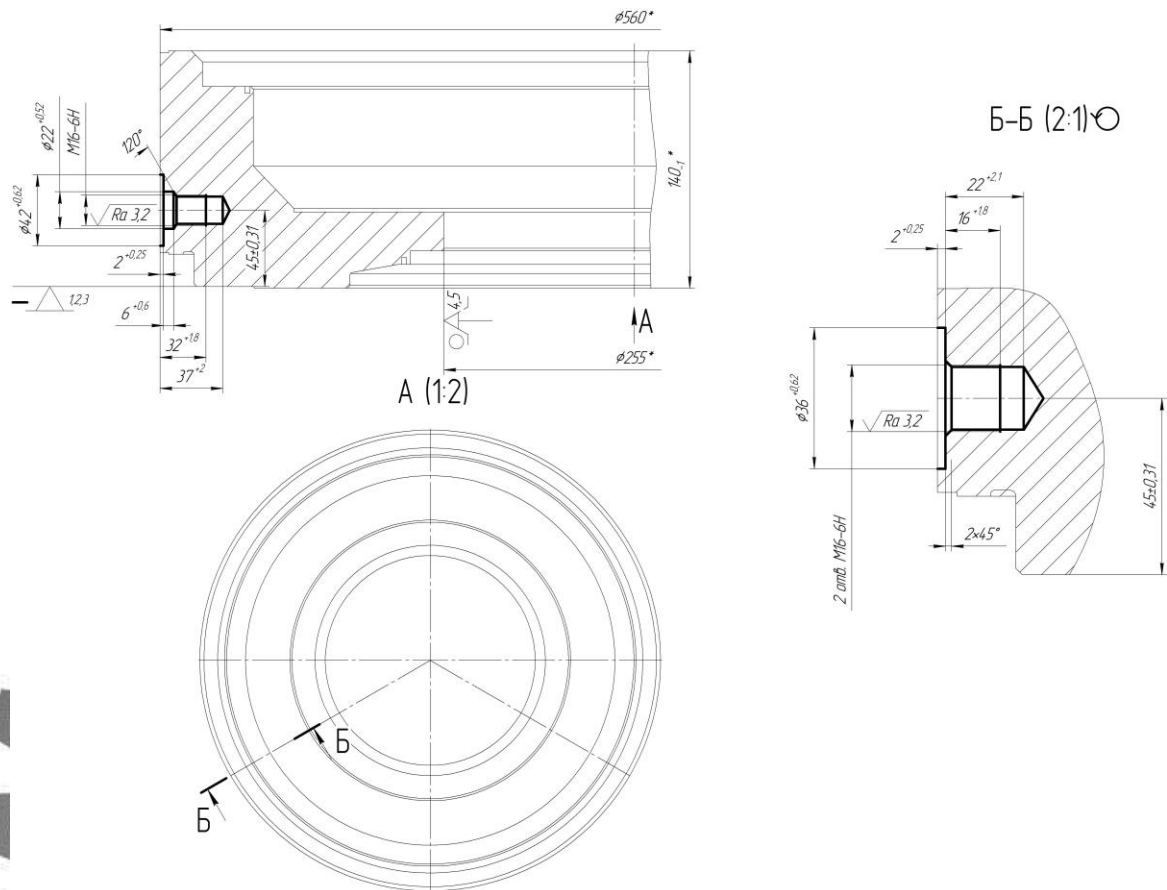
Схема базування заготовки на комплексній операції (другий варіант)
